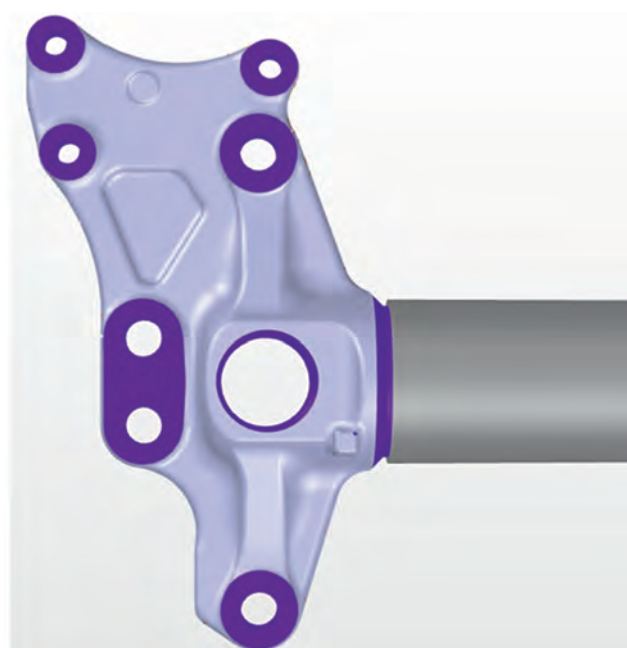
GJS – Flansch mit gestecktem Tragrohr
